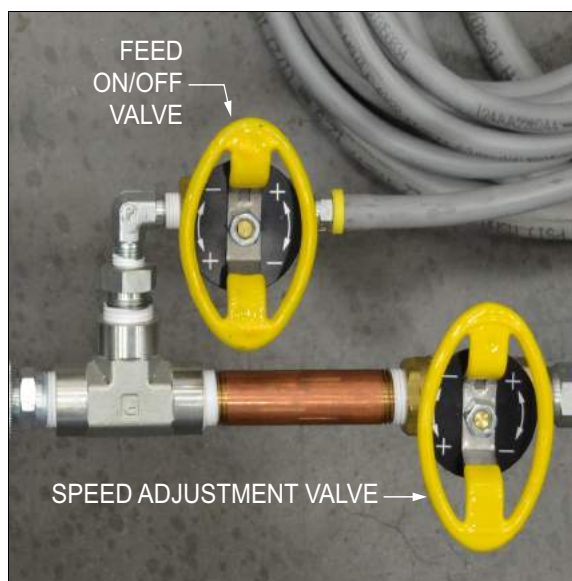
SOUPAPES D'USINAGE PNEUMATIQUE
